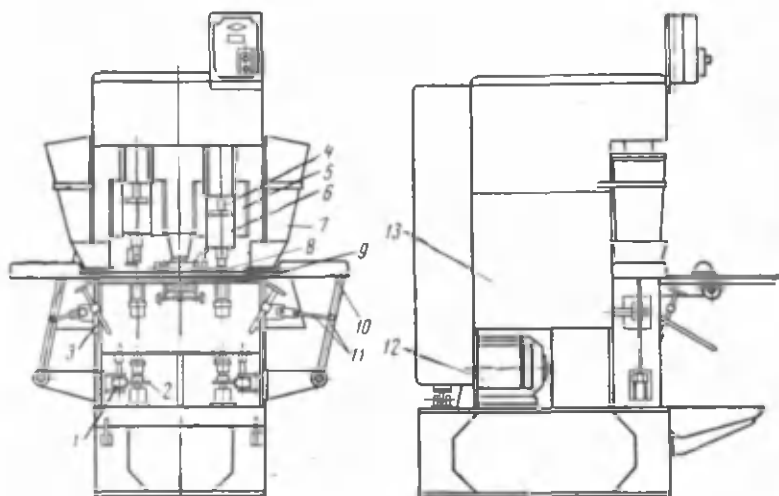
Эксцентриковый пресс для изготовления агломератов галетных элементов:
